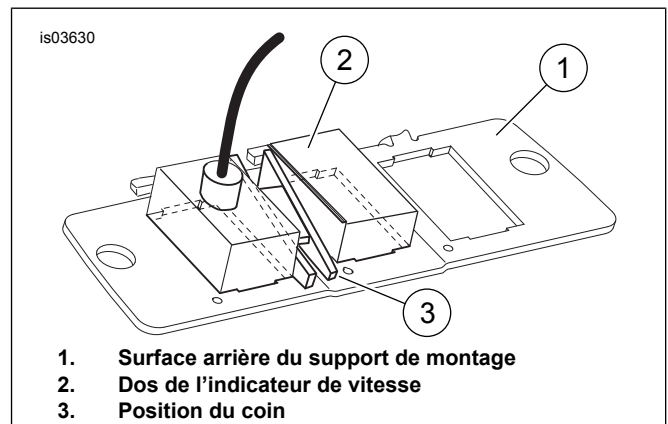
Vue arrière de l'ensemble de support de montage et d'indicateur de rapport
